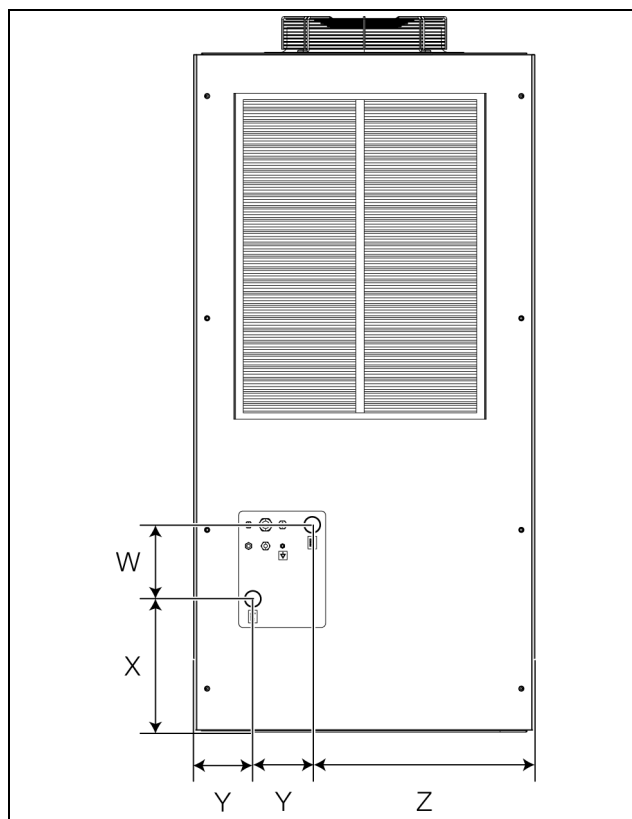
Dimensions (raccordements d'alimentation) de la face arrière sans socle (représenté 3335.790)
